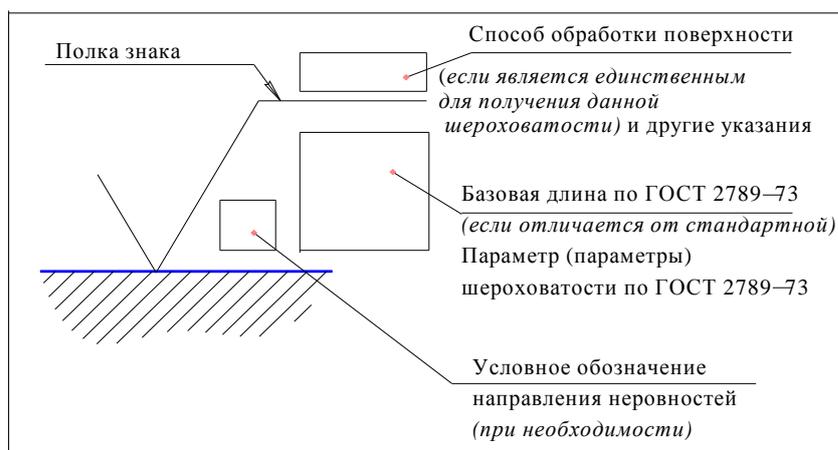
Структура обозначения шероховатости поверхности [21]
